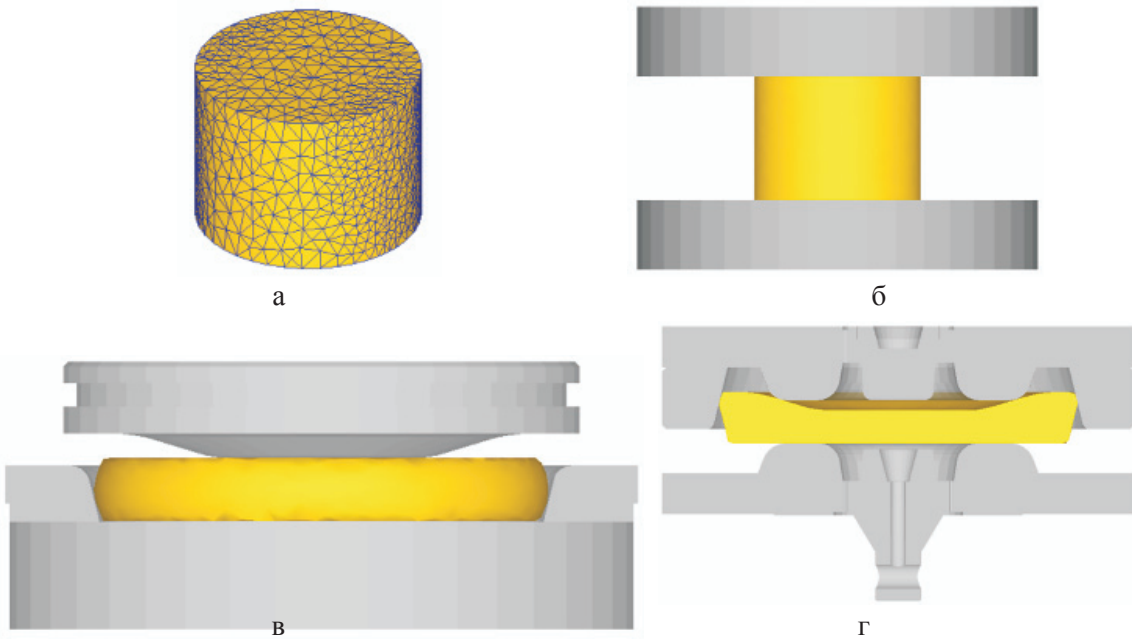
Картины математического моделирования операций горячей объемной штамповки колесной заготовки: а – исходная заготовка с построенной конечно-элементной сеткой; б – предварительная осадка; в – осадка и разгонка; г – формовка
